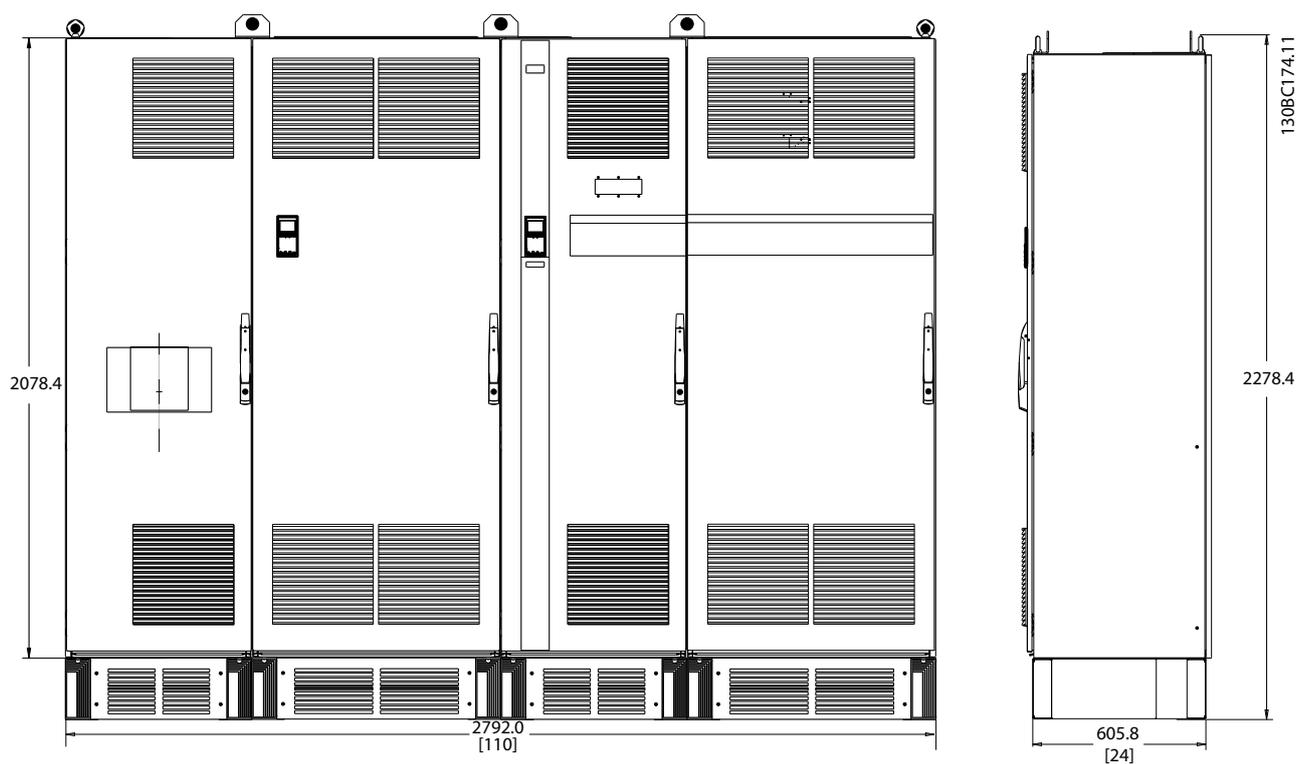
Типоразмер F18, вид спереди и сбоку
